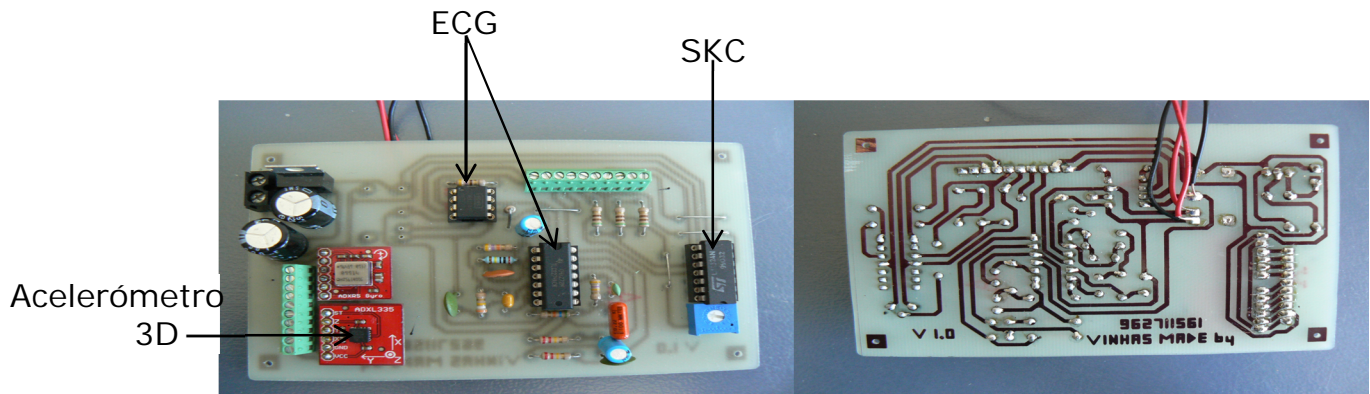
Montagem PCB com ECG, SKN e Acelerómetro
